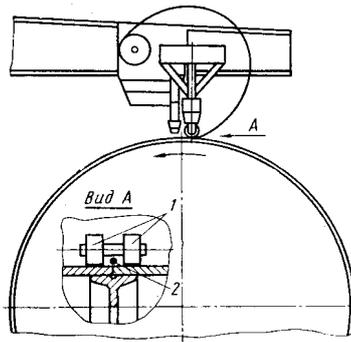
Схема приспособления для прижатия кромок к подкладному кольцу перед сварочной головкой:
